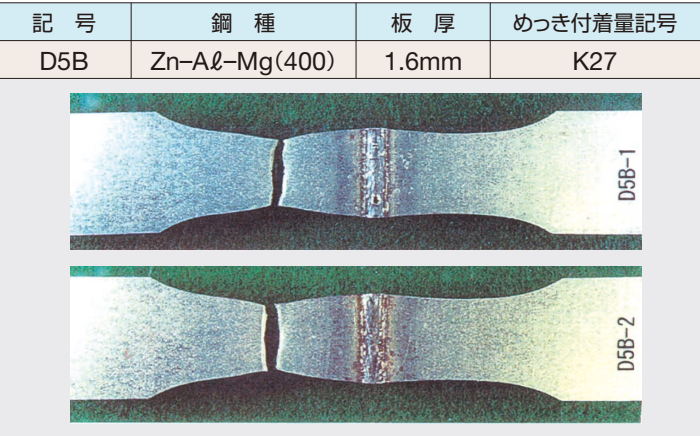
板厚1.6mm材の重ね隅肉溶接継手引張試験での破断状況
